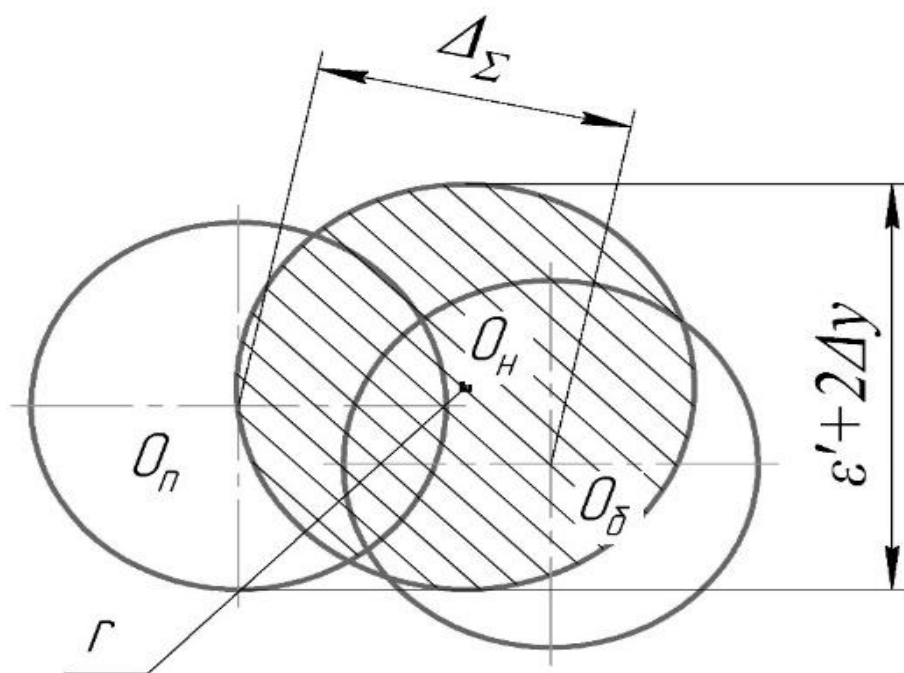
Контур перемещения торца ниппеля (присоединяемой детали  $O_n$ ) перед началом сопряжения с резьбовой поверхностью корпуса ( $O_b$ )
